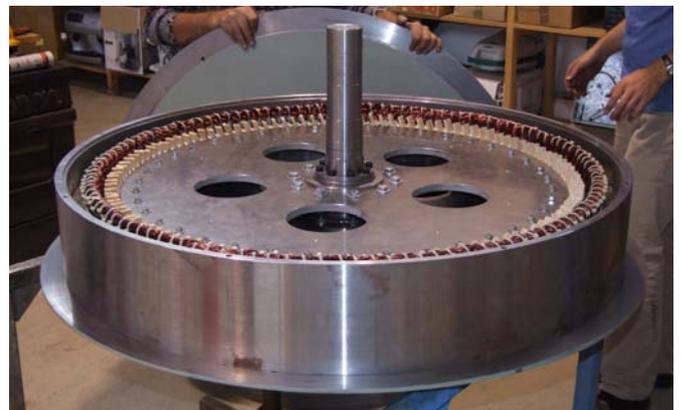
Rotor und Stator vor der Montage des Lagerschilds
